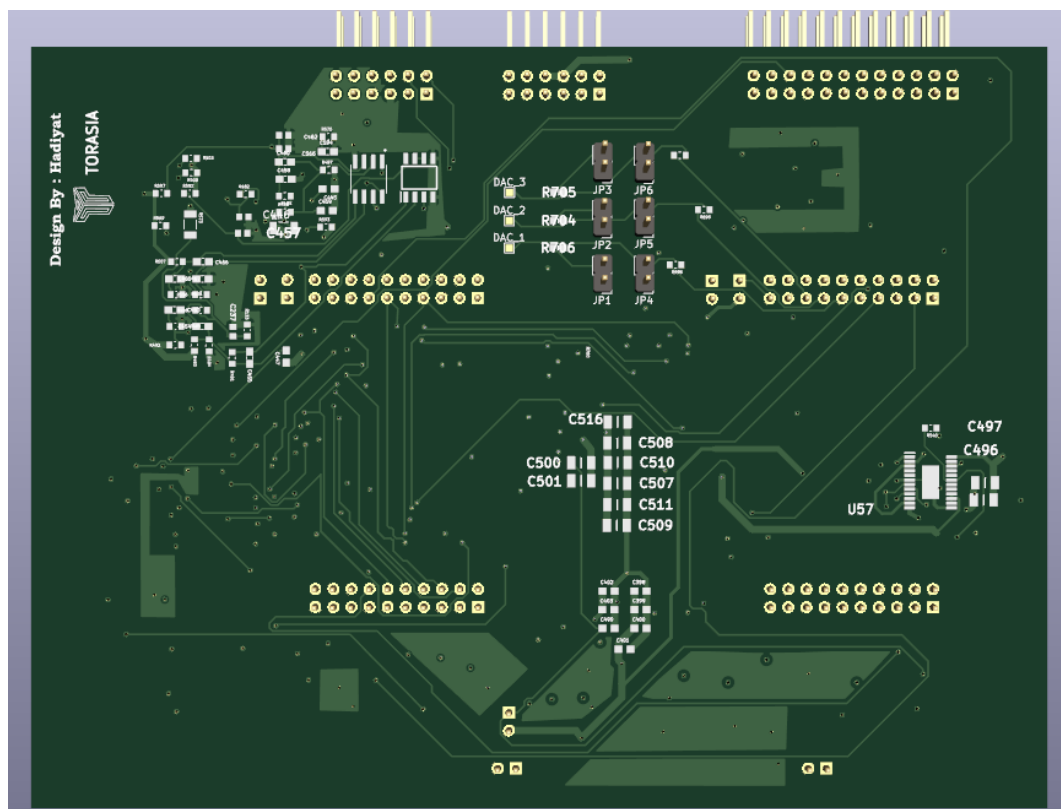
14 Tampilan 3D PCB Layer Atas pada Power Board/Board Utama
